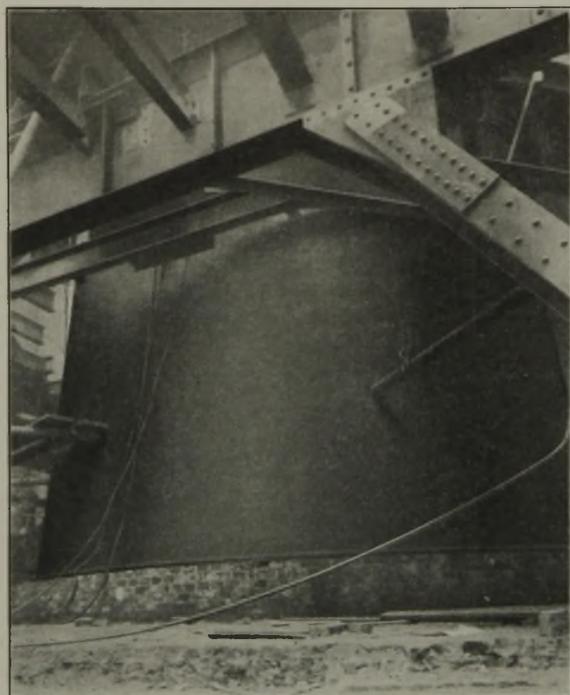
Gestellpanzer aus Siemens-Martin-Walzblech, elektrisch geschweißt.
